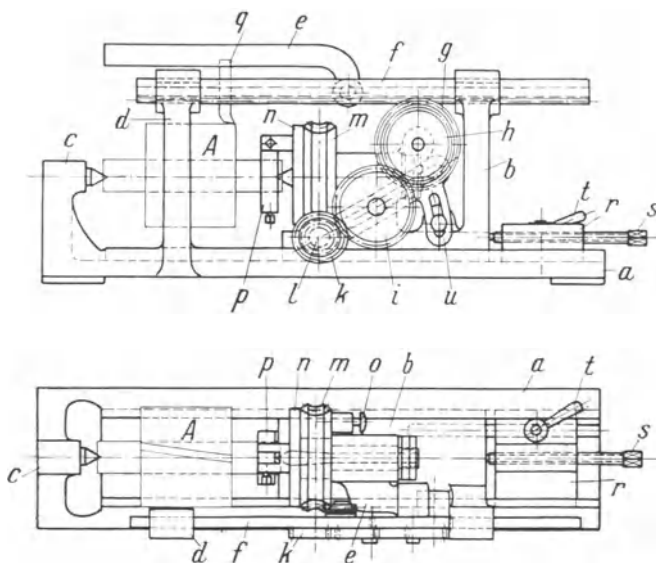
Drallnuten-Hobelvorrichtung auf Shapingmaschinen.
